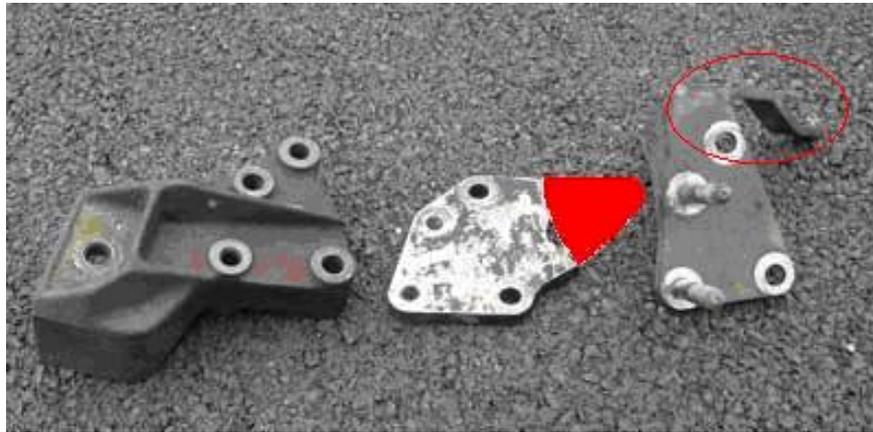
(à gauche le support moteur, au milieu la plaque support d'AX et à droite la plaque de 205)
